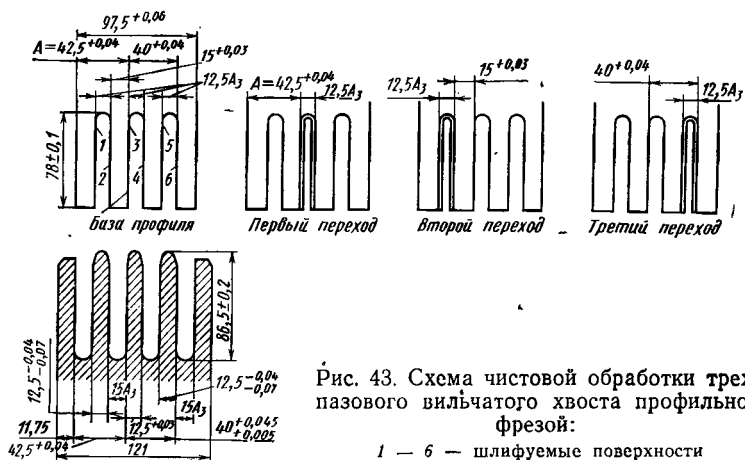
Схема чистовой обработки трехпазового вильчатого хвоста профильной фрезой:
